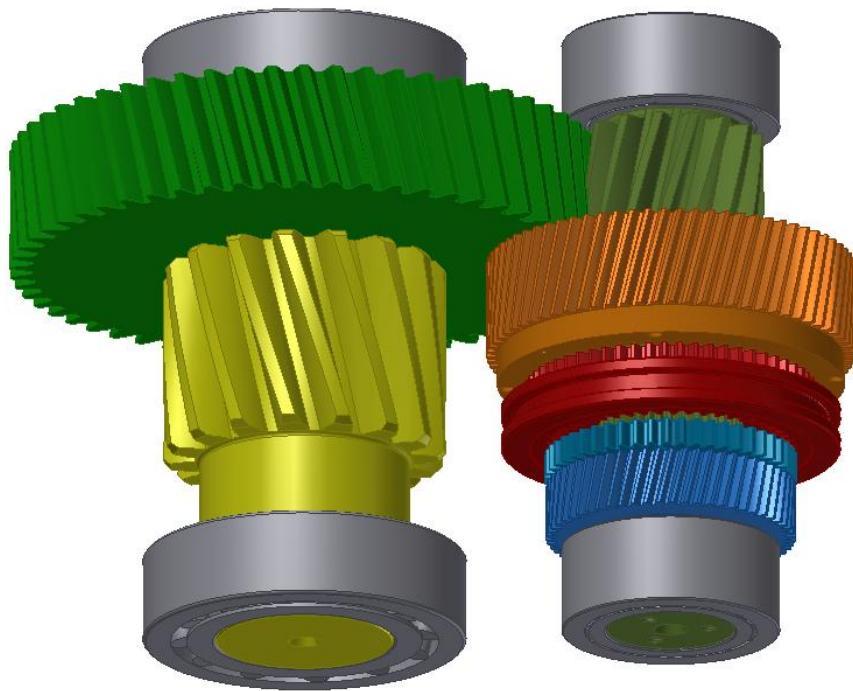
3D model soukolí 1,2; soukolí 3,4; přesuvná spojka
